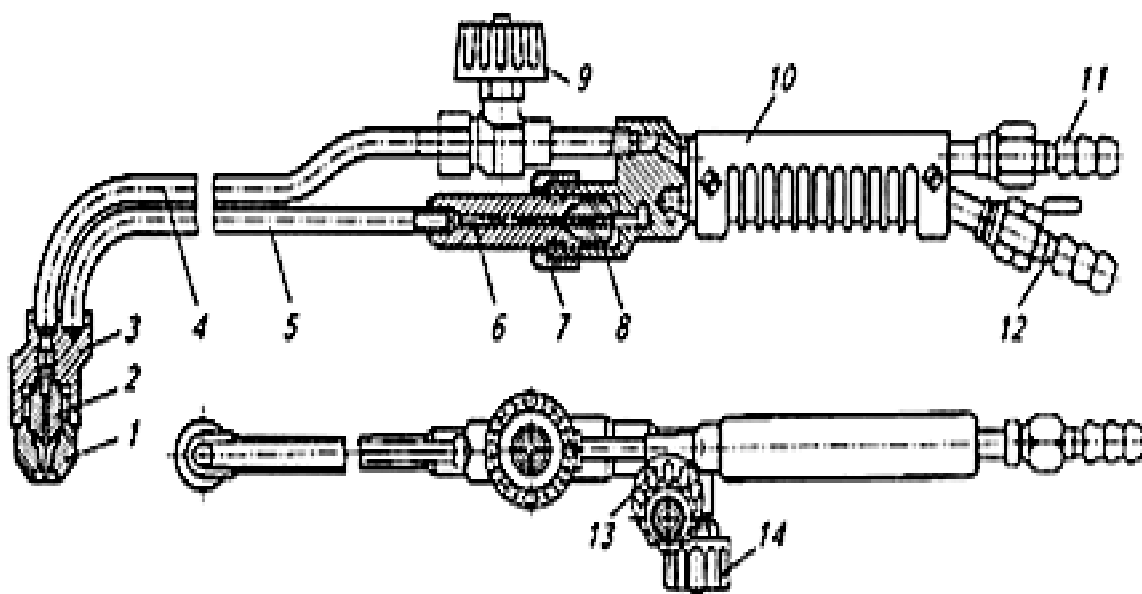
Ручной ацетилено-кислородный резак: 1, 2 – мундштук; 3 – головка; 4, 5 – трубки; 6 – камера; 7 – гайка; 8 – инжектор; 9, 13, 14 – вентили; 10 – рукоятка; 11, 12 – штуцеры
